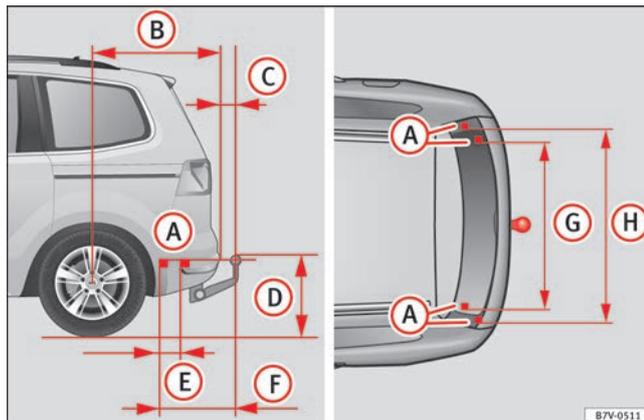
Maße und Befestigungspunkte zum Nachrüsten einer Anhängervorrichtung.
